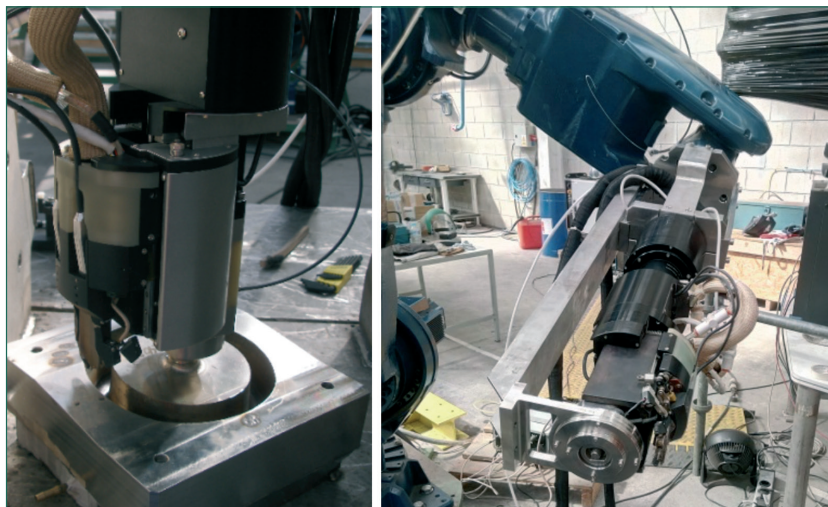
Cabezal de soldadura de *biscuit*.
